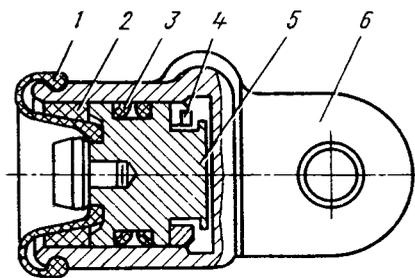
Колесный цилиндр переднего барабанного тормоза автомобиля ГАЗ-24-10: 1 — защитный чехол; 2 — порошковое кольцо; 3 — уплотнительное кольцо; 4 — упорное кольцо; 5 — поршень; 6 — корпус
